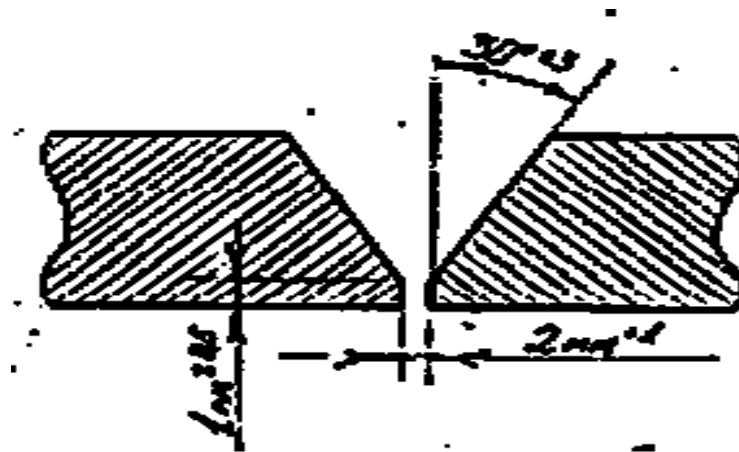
Підготовка кромки стикового з'єднання С 17
